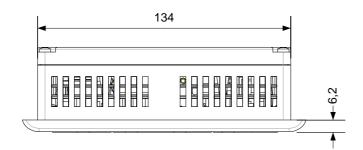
Dimensiones principales del OP°77A y del OP°77B
